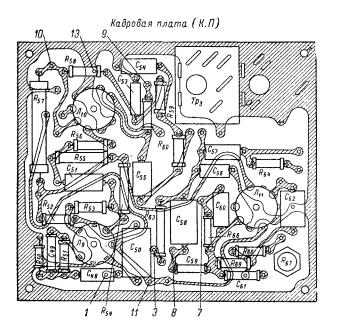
Расположение деталей на плате кадровой развертки телевизора «Старт-3».
